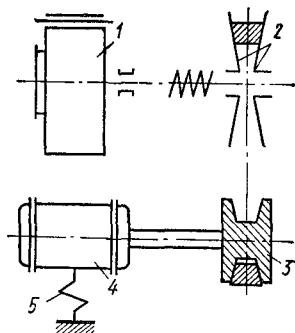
Схема ременного вариатора частоты вращения рабочего колеса вентилятора
